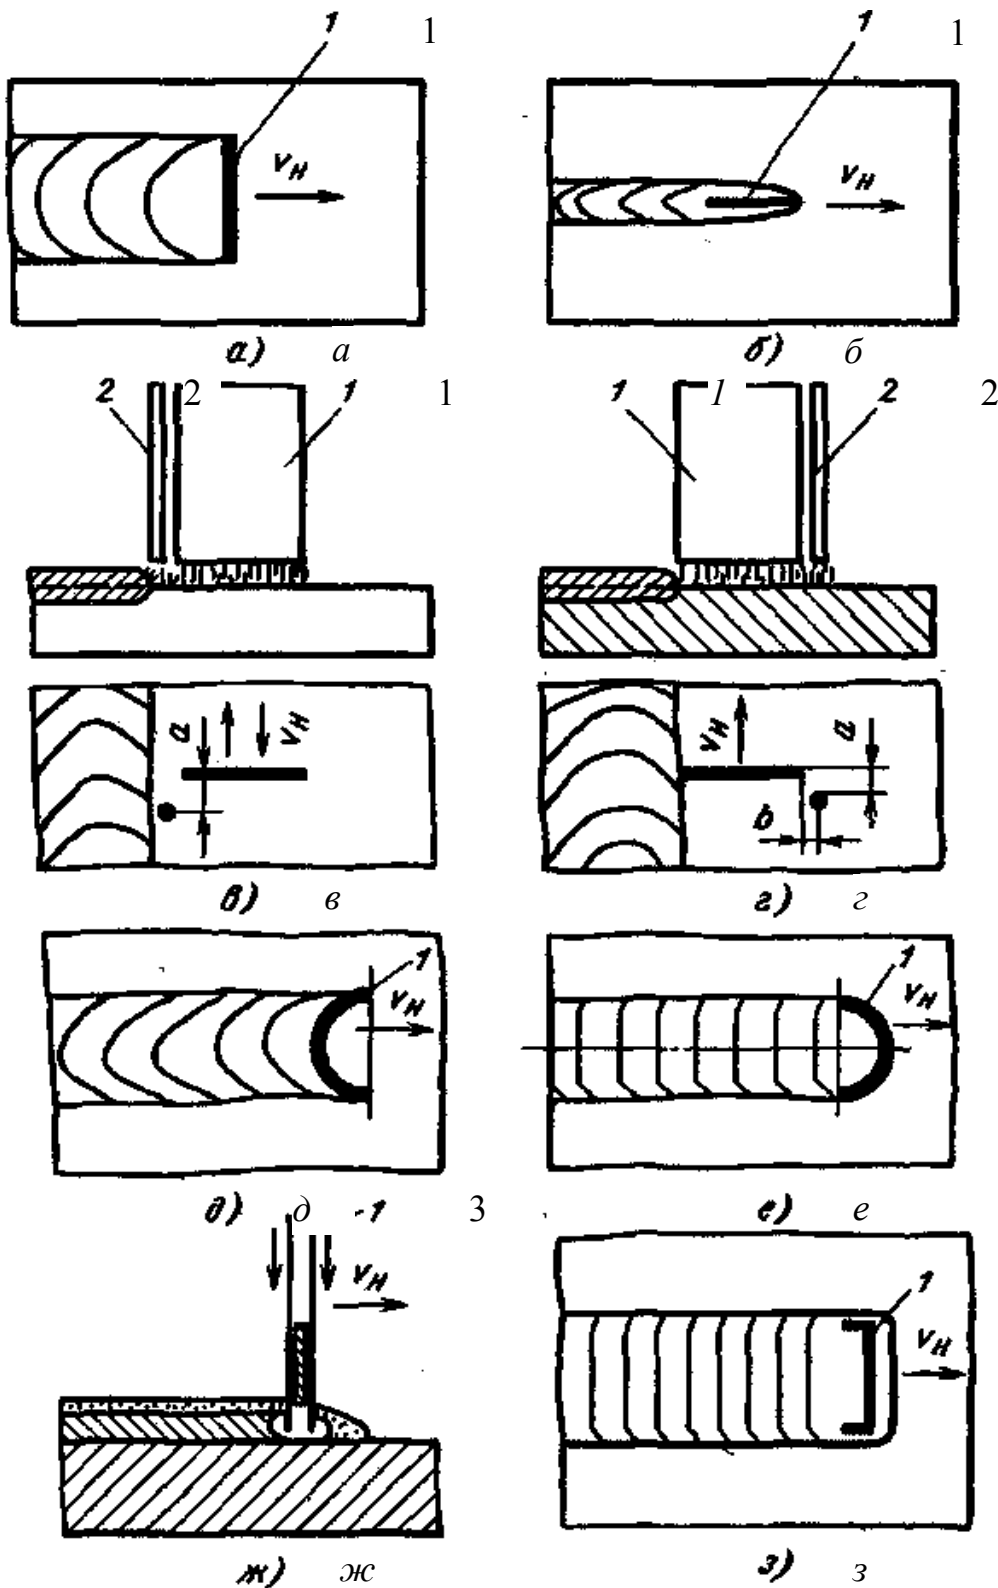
Схема наплавлення дротом і стрічкою: 1 — електродна стрічка; 2 — електродний дріт; 3 — швидкість зварювання
